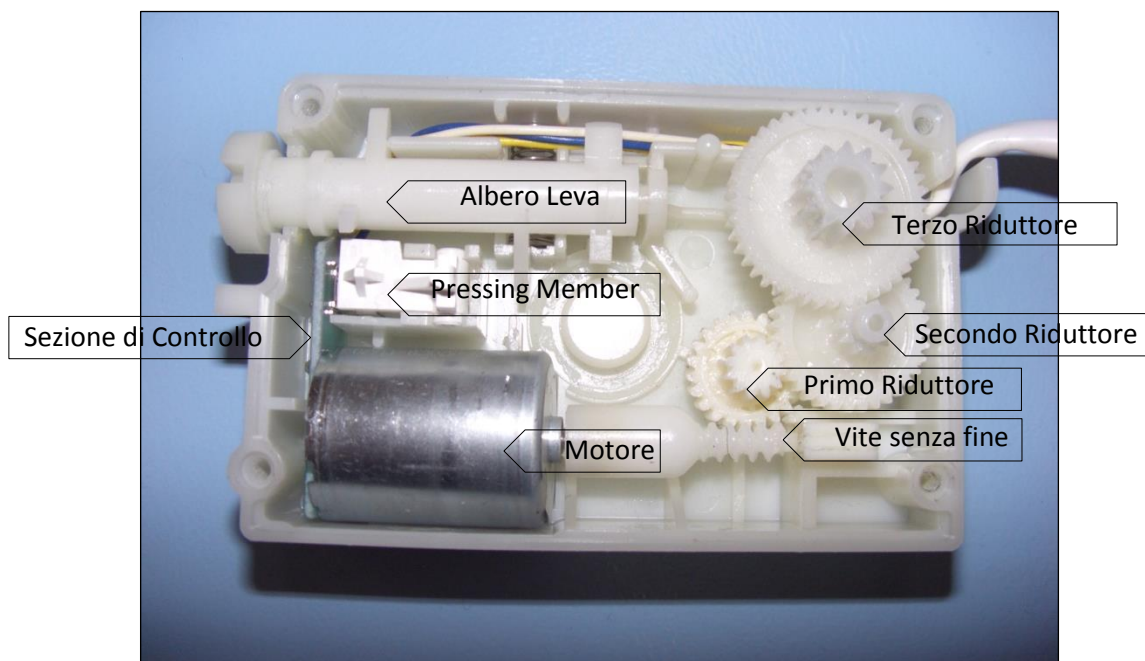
Vista interna della gear-box (parte del sistema di trasmissione, motore, sezione di controllo, pressing member e albero leva)
